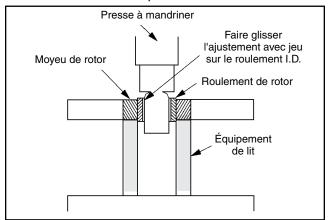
Dépose du roulement de rotor en carbure de tungstène
